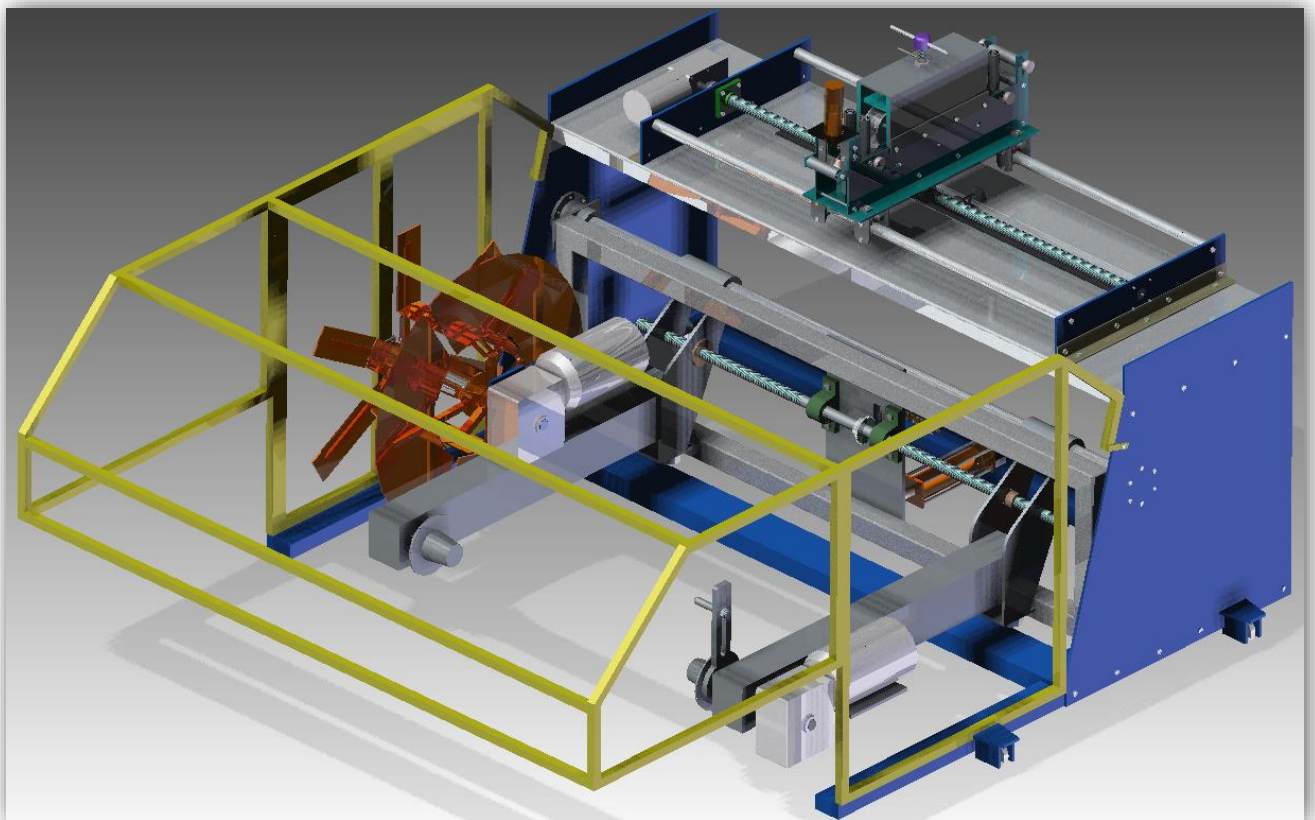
Diseño de la Máquina Devanadora en Solid Edge St5
